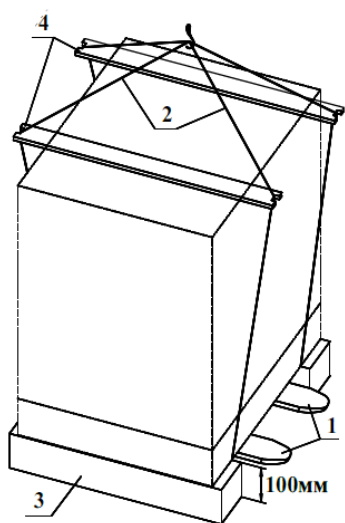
Схема строповки ККБ малых типоразмеров
